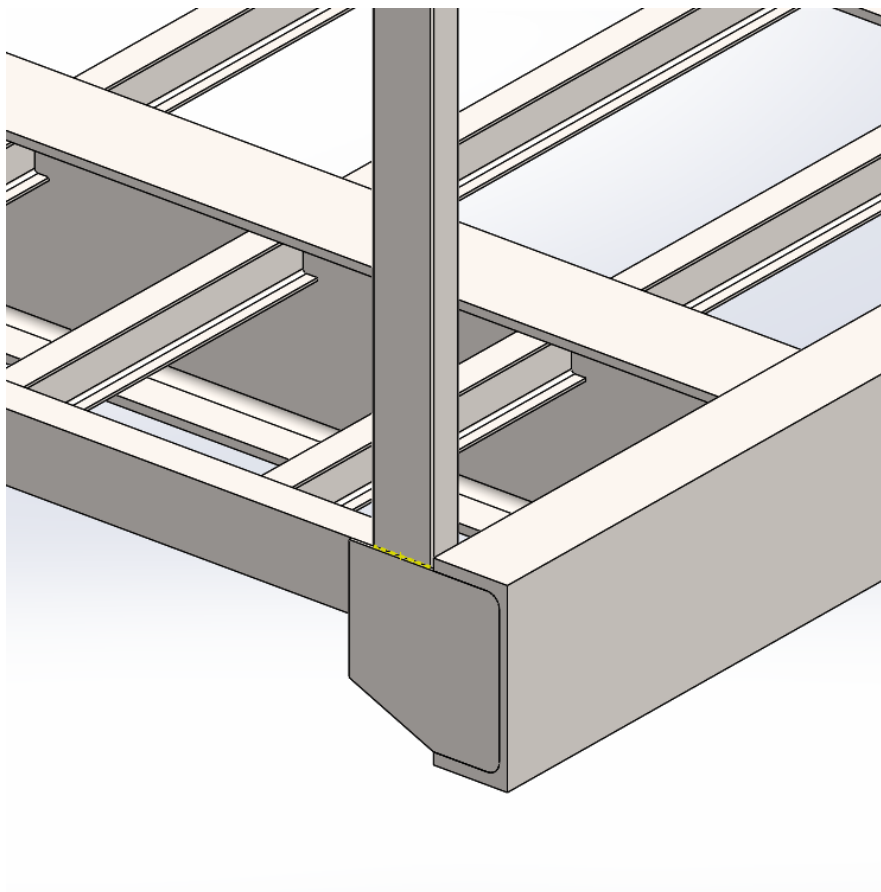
Detalle de soldadura de pilar trasero.
